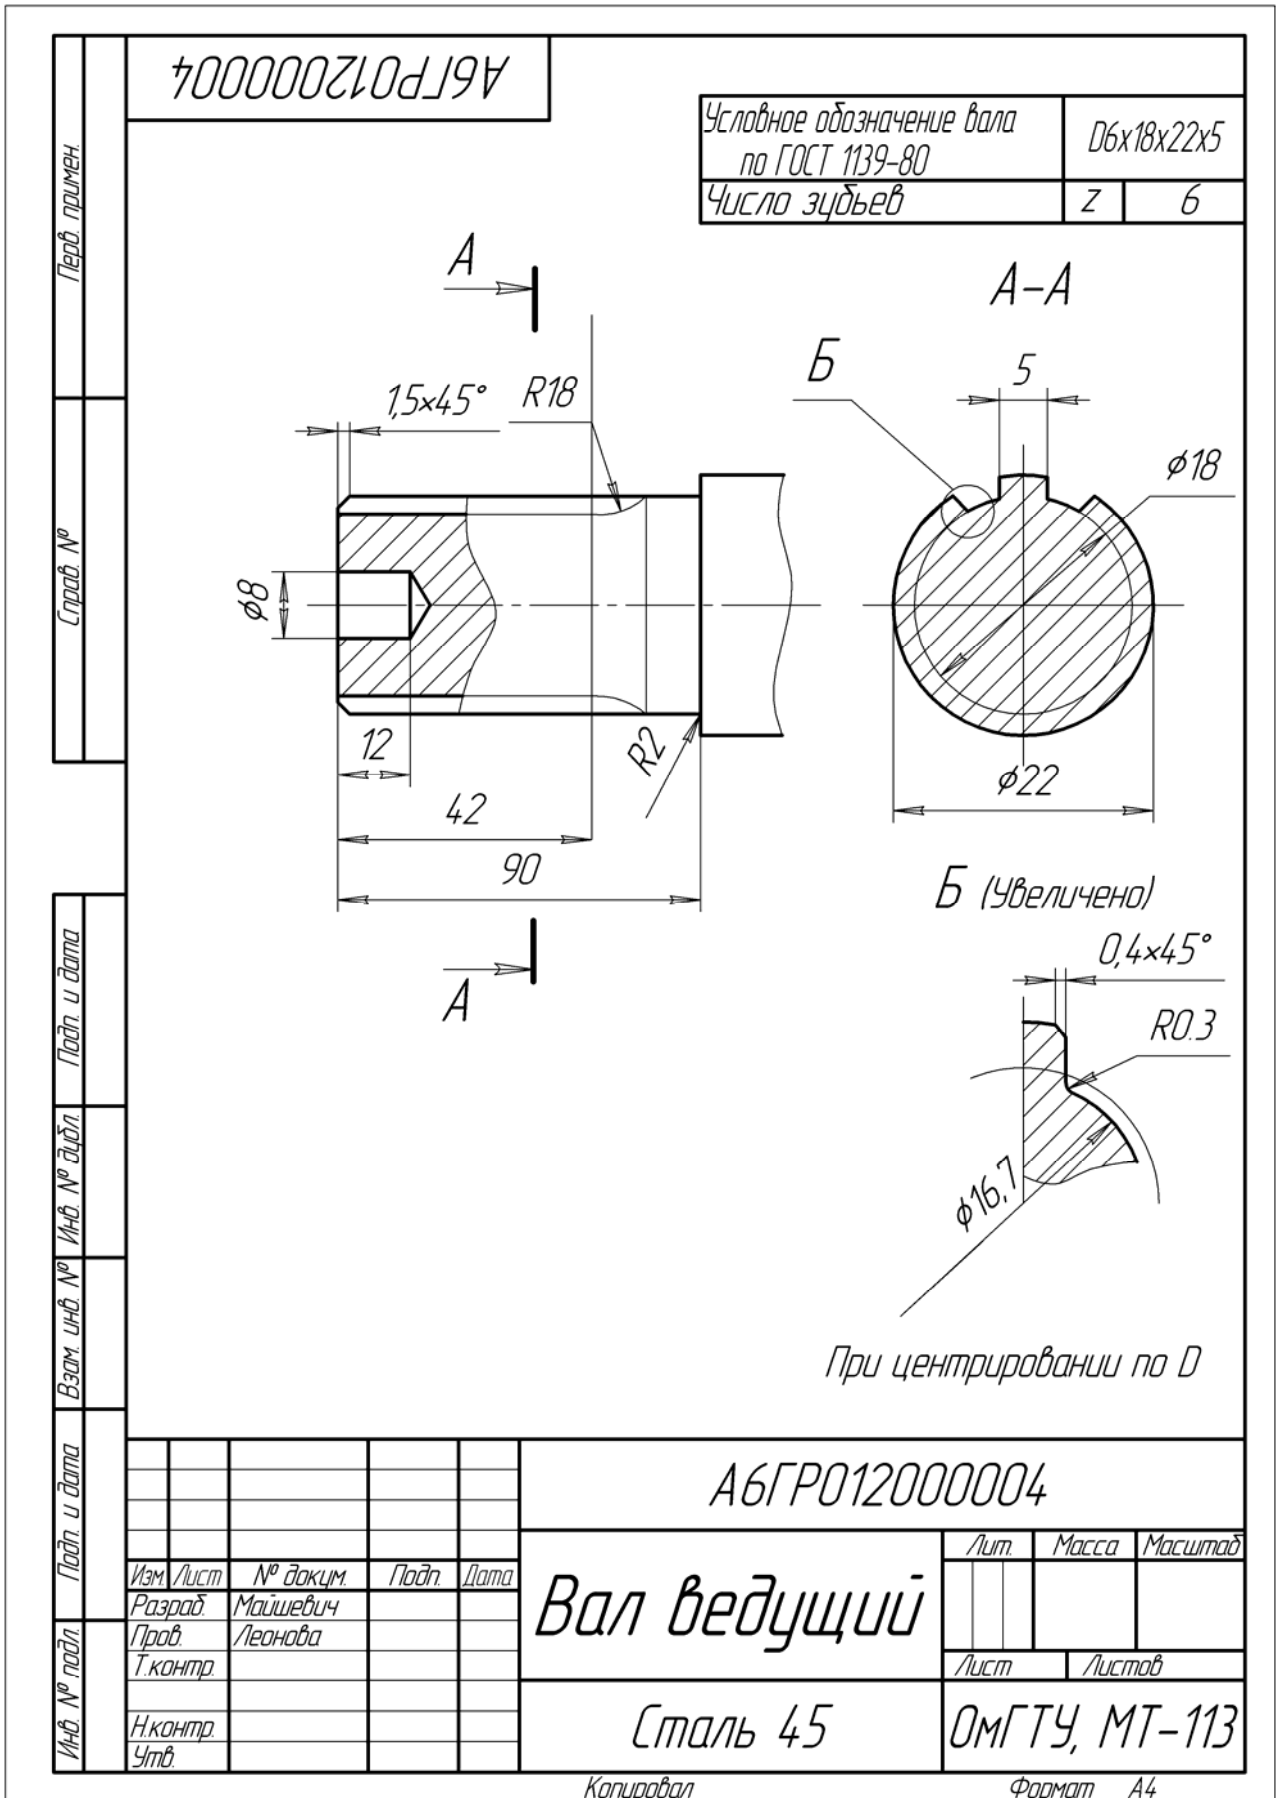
Рабочий чертеж хвостовика шлицевого вала
